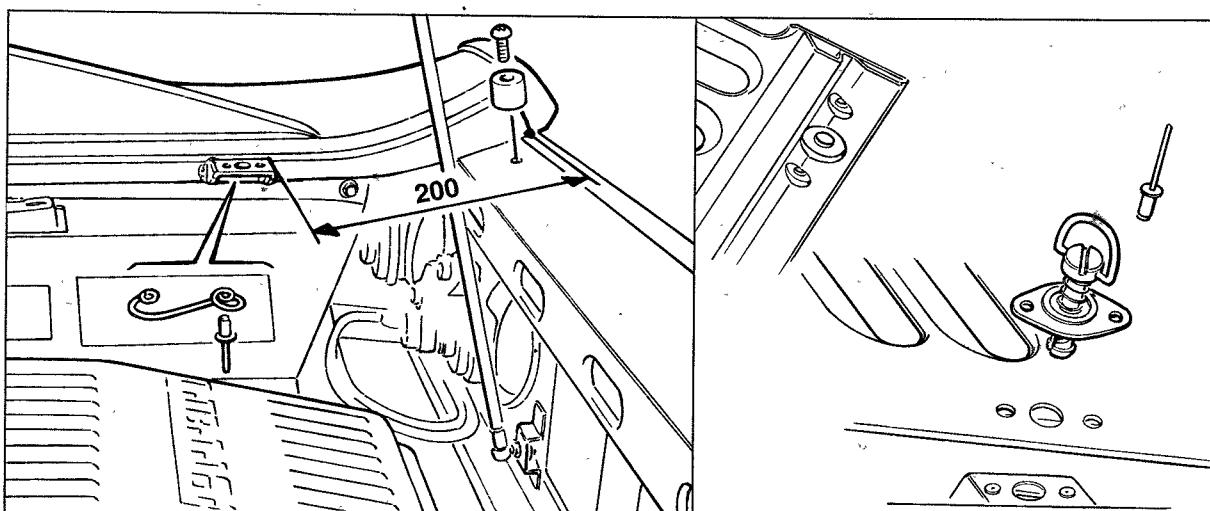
Fissaggio molle e tamponi di chiusura cofano
